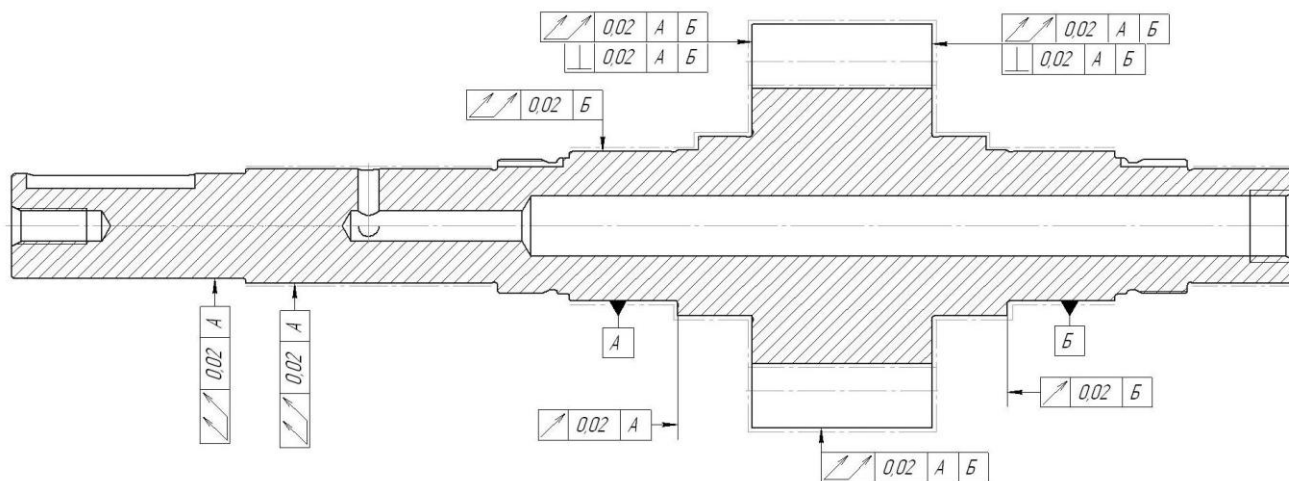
Відхилення форми та розташування поверхні деталі вал шестерня
